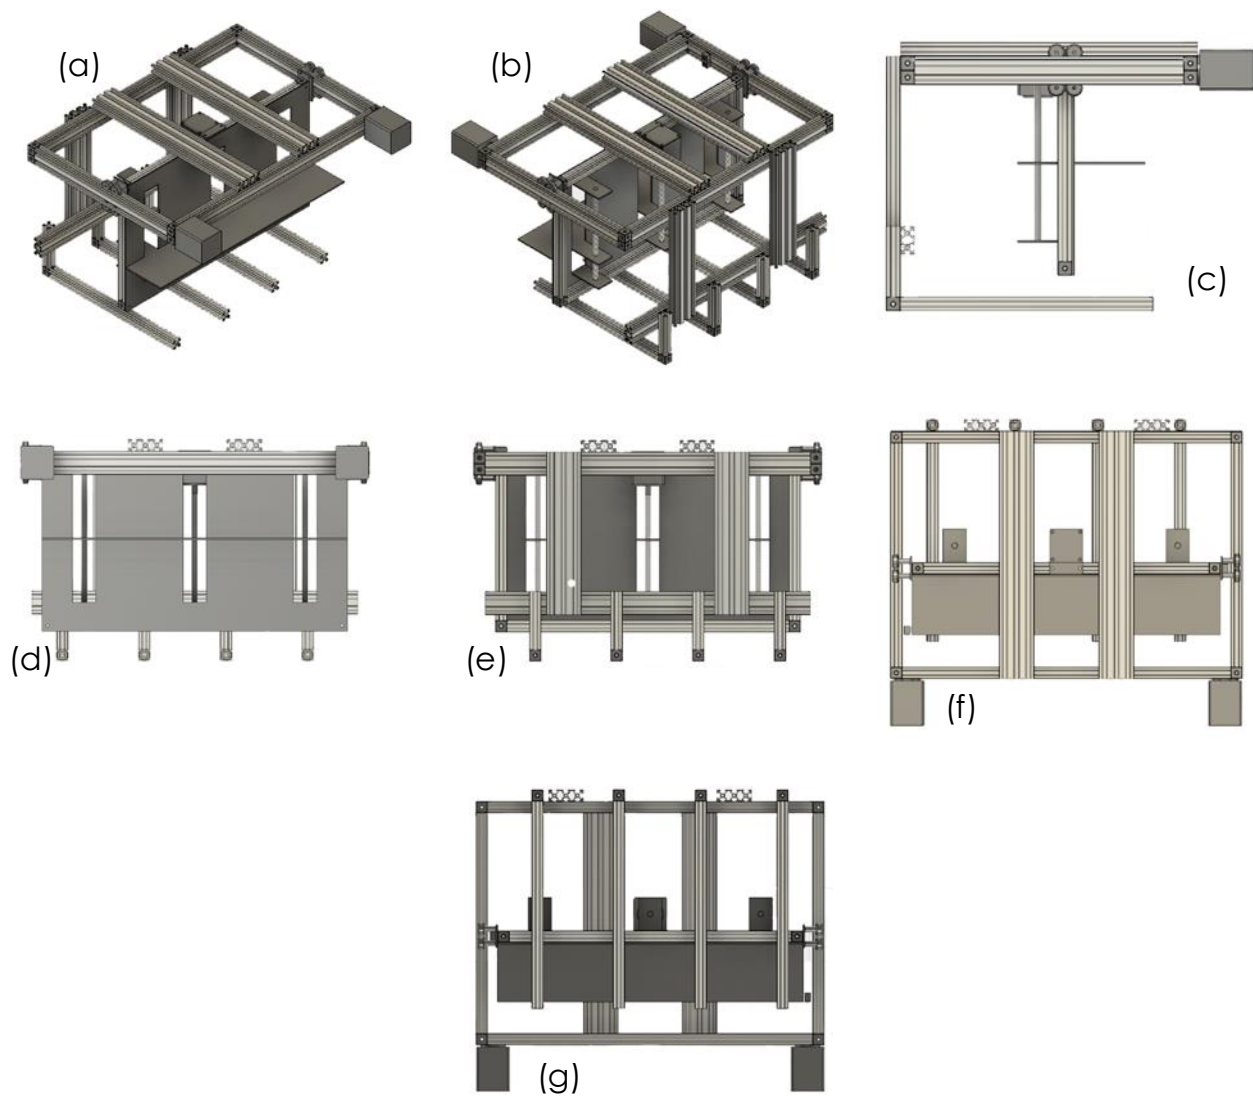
Modelo CAD de gripper. (a) Vista isométrica frontal. (b) Vista isométrica trasera. (c) Vista lateral. (d) Vista frontal. (e) Vista trasera. (f) Vista superior. (g) Vista inferior.
